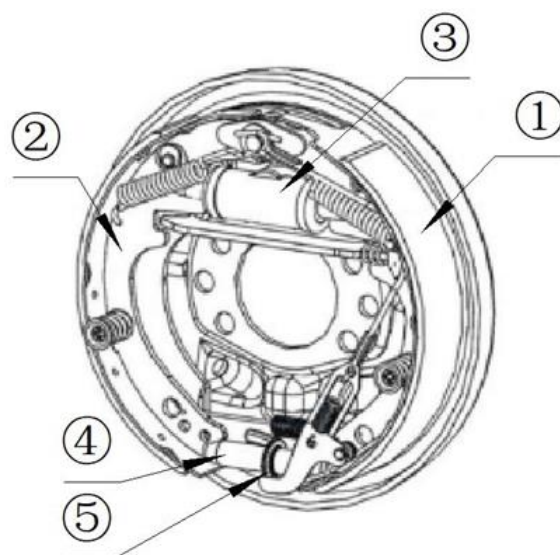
Схема конструкции тормоза вилочного погрузчика:
